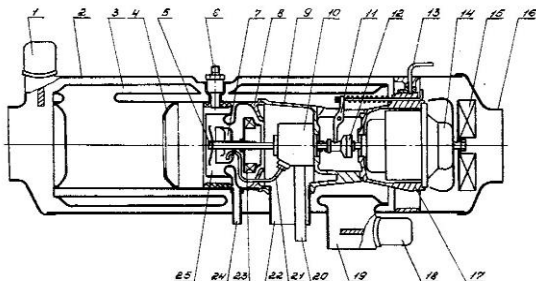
Отопительно-вентиляционная установка типа ОВ-65
